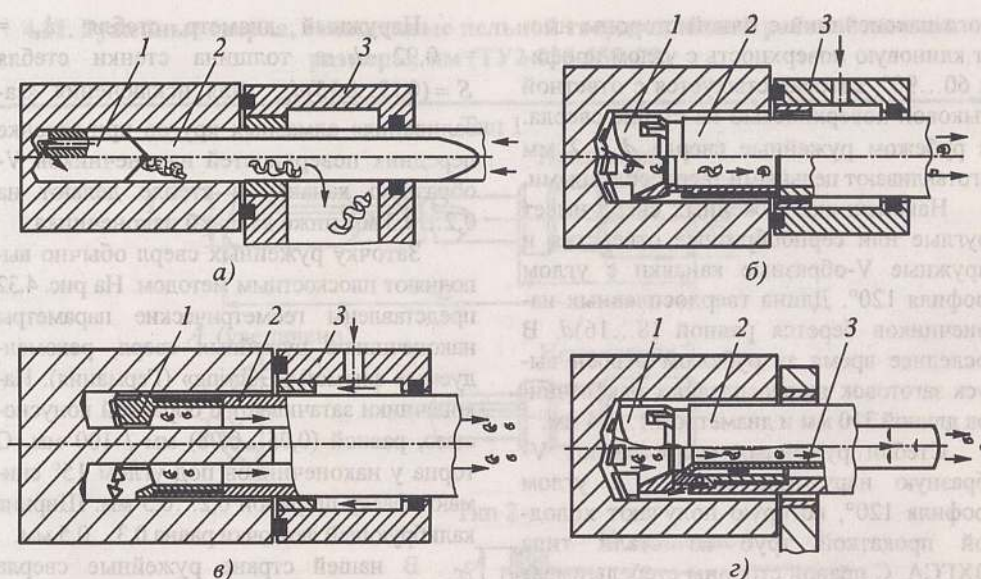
Схемы обработки глубоких отверстий инструментами одностороннего резания: а – ружейное сверло; б – сверло типа БТА; в – кольцевое сверло типа БТА; г – эжекторное сверло
